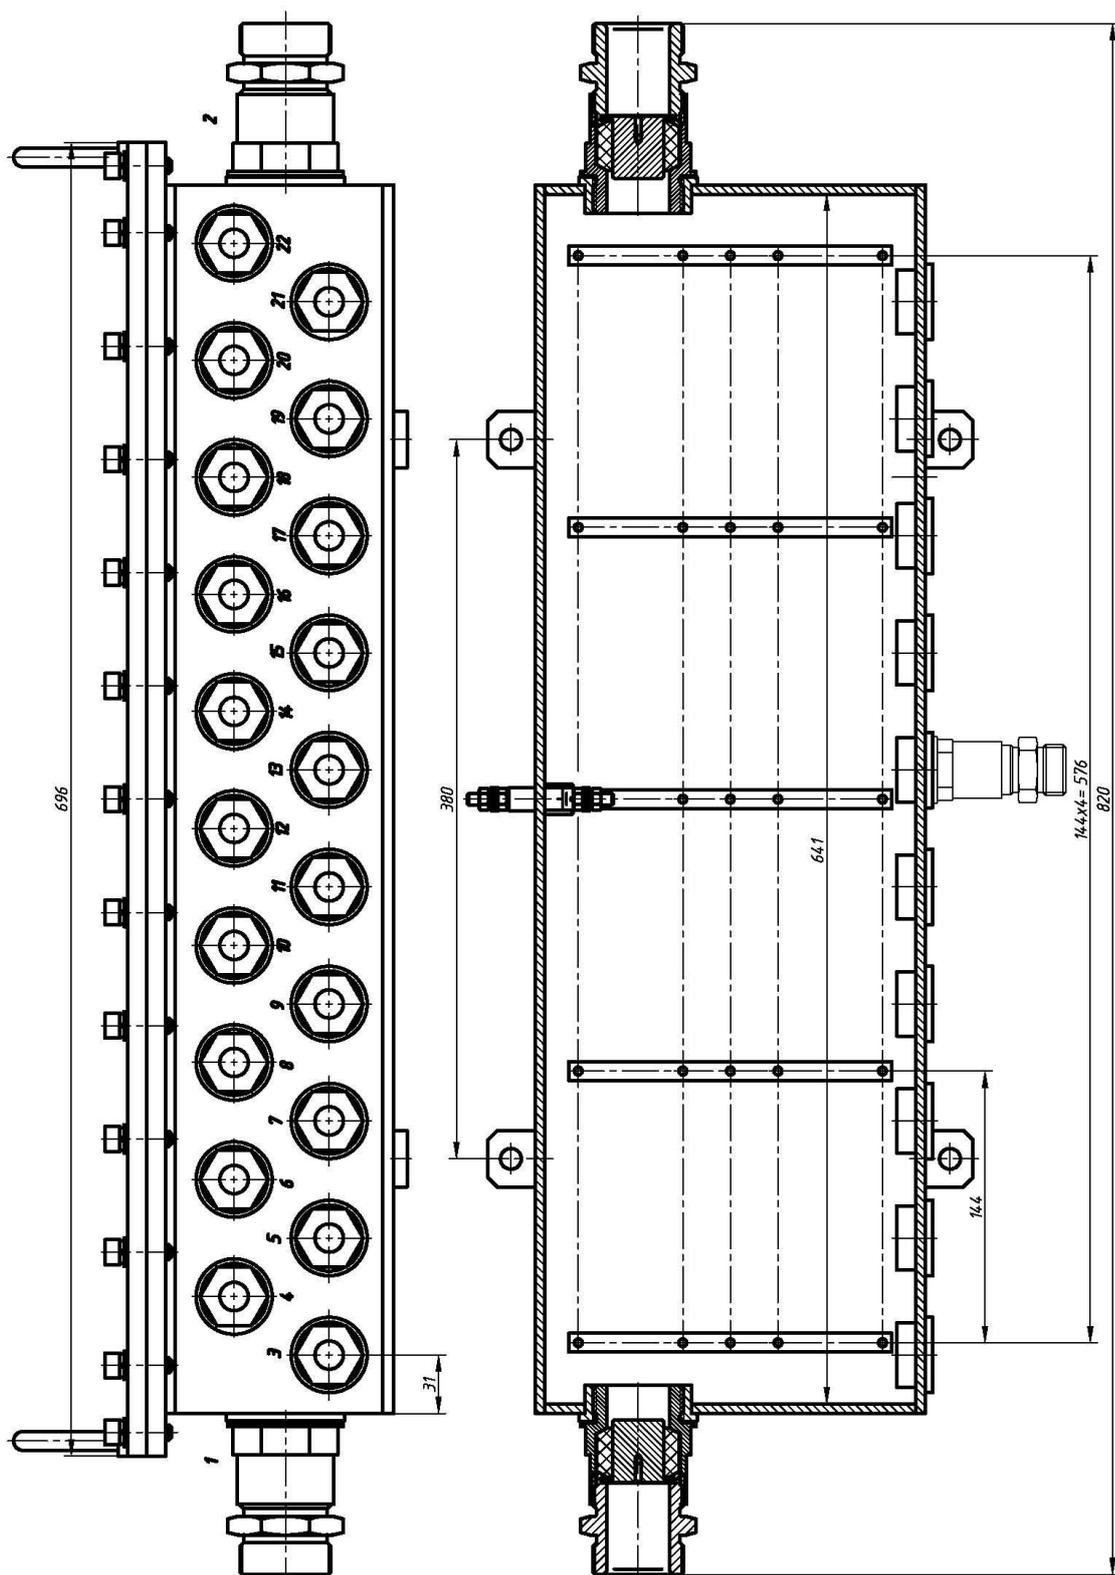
Габаритные, установочные и присоединительные размеры базовой коробки ExКСУВ-ПС700. Остальное смотреть рисунок В.1. По умолчанию в патрубках №№1 и 2 резьба G1 1/2, в патрубках №№ 3-22 резьба G3/4.
